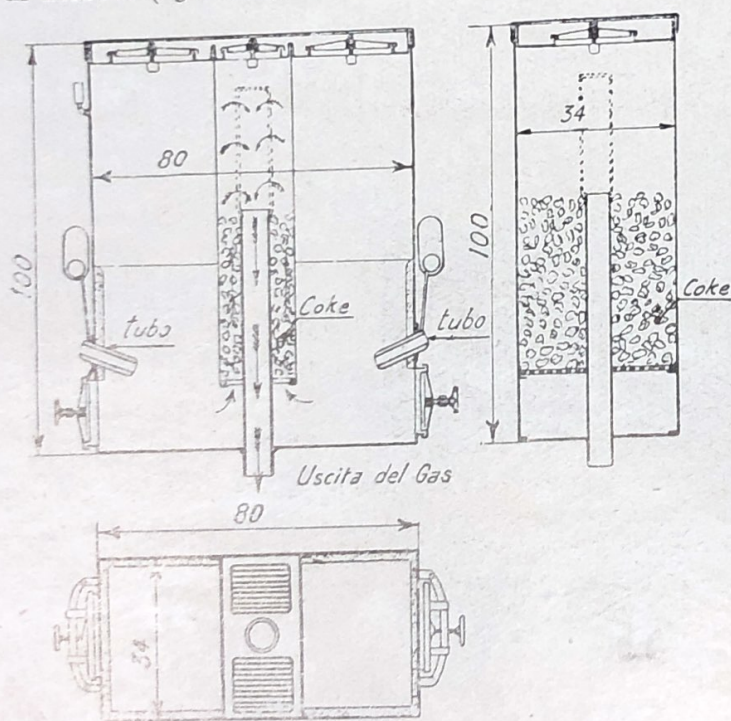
SEZIONE E PIANTE DEL GASSOGENO GOHIN APPLICATO ALLE VETTURE SUDDETTE.
